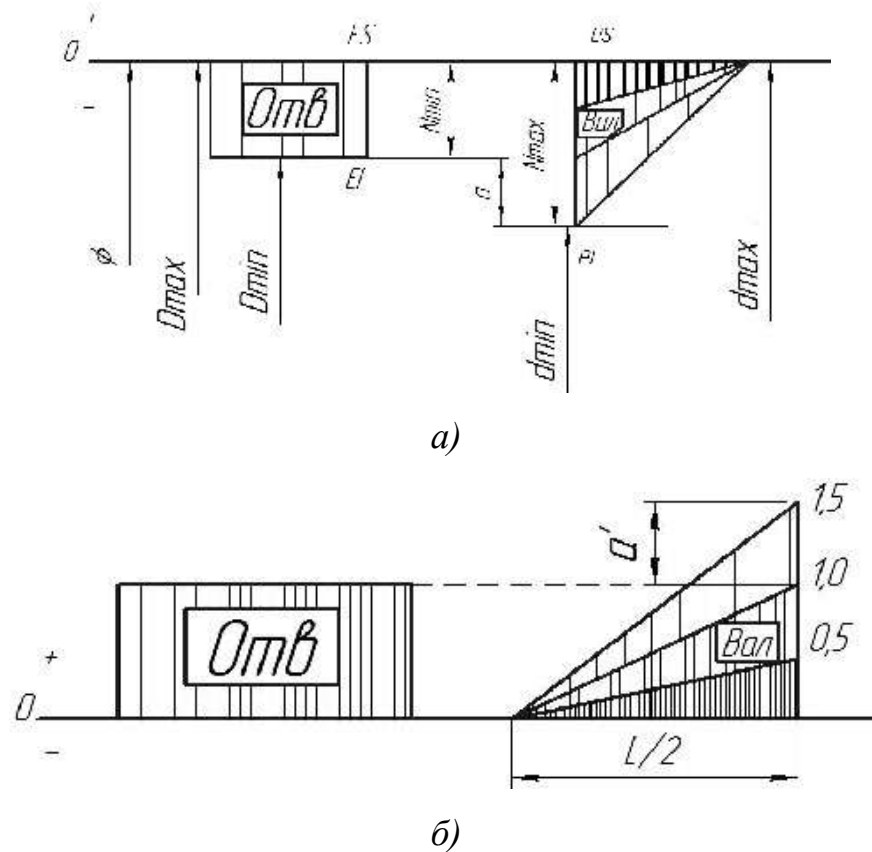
Схема полів допусків для конічної пружини:
